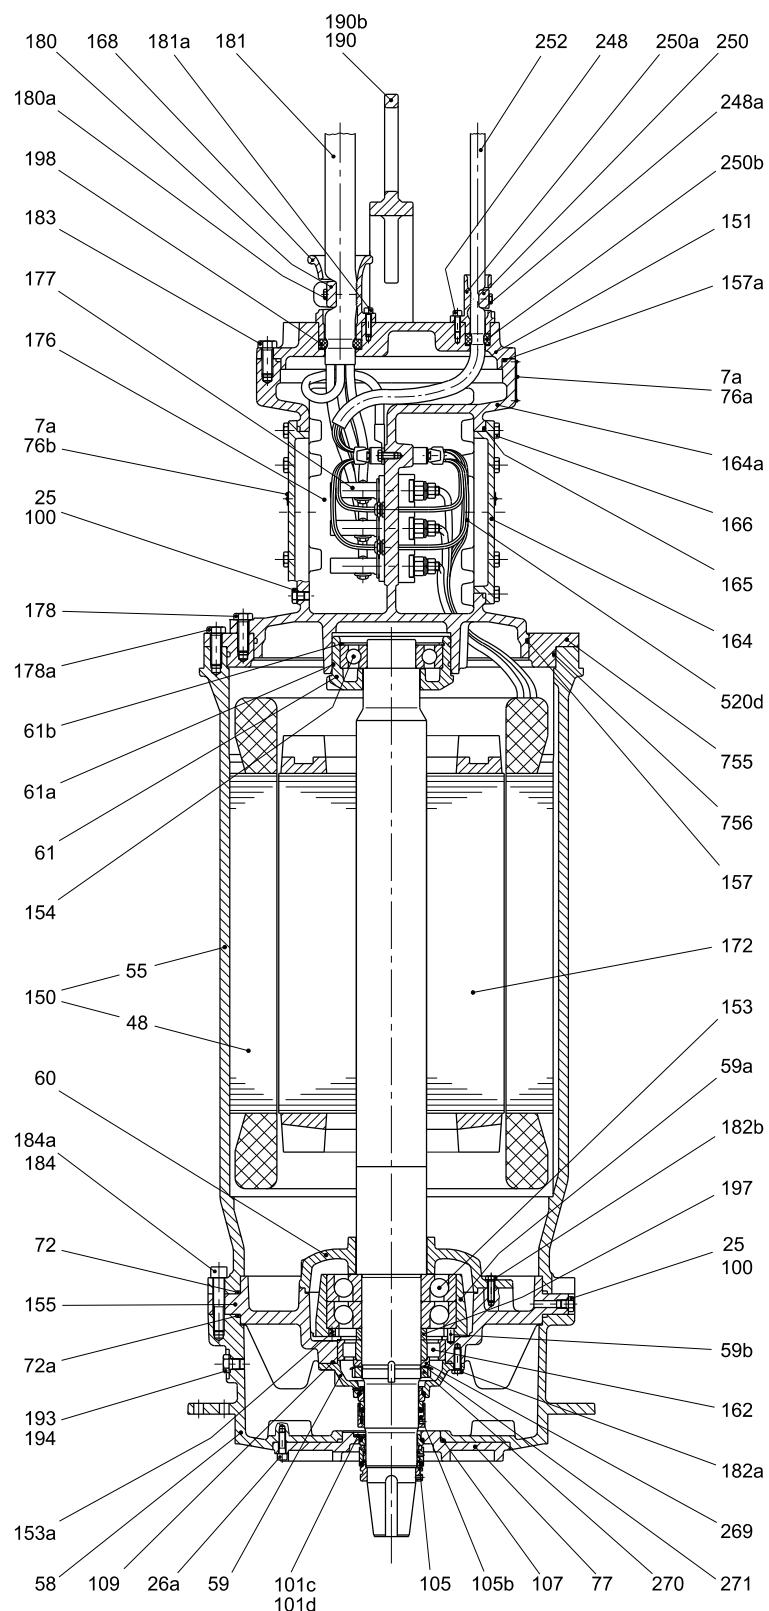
Типоразмер 74 для установки в обсадной трубе
